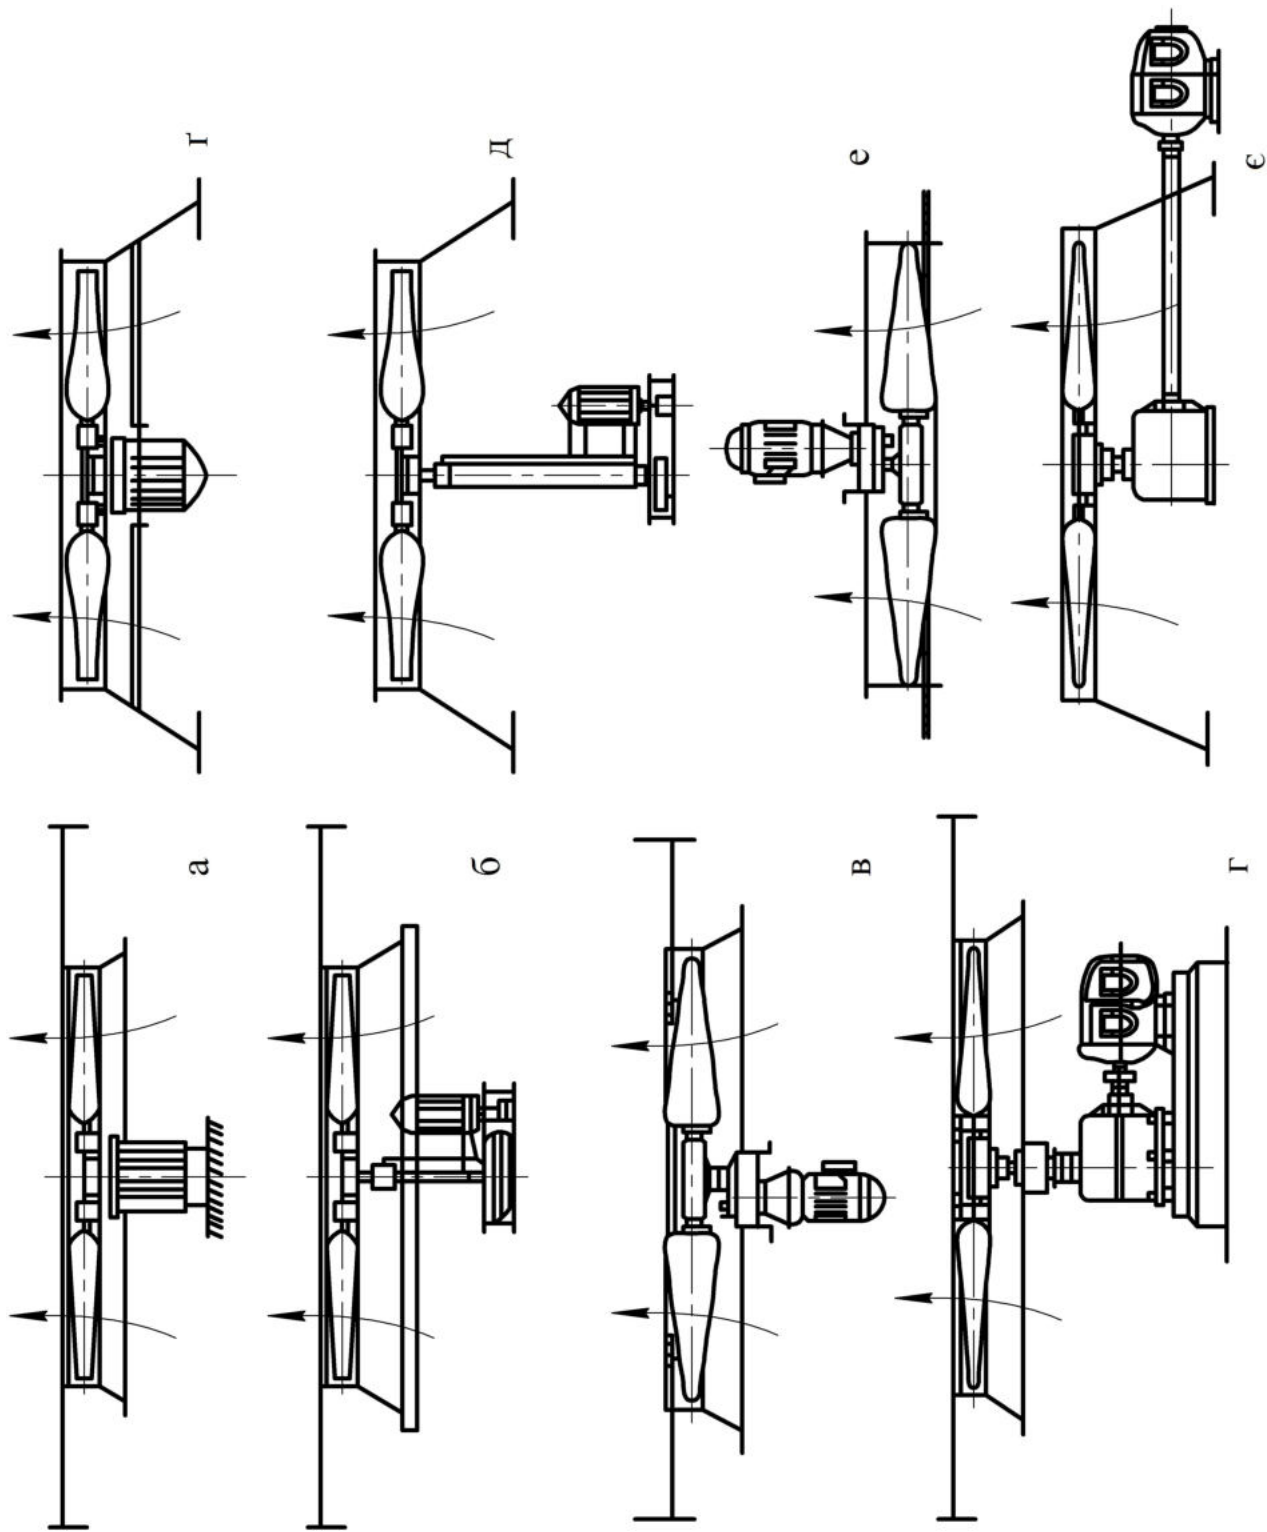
Приводи АПО нагнiтального (а-г) та витяжного (г-є) типiв: а, г – прямиї; б, д – клинопасовий; в, е – редуктор iз паралельними валами; г, є – редуктор iз перпендикулярними валами
